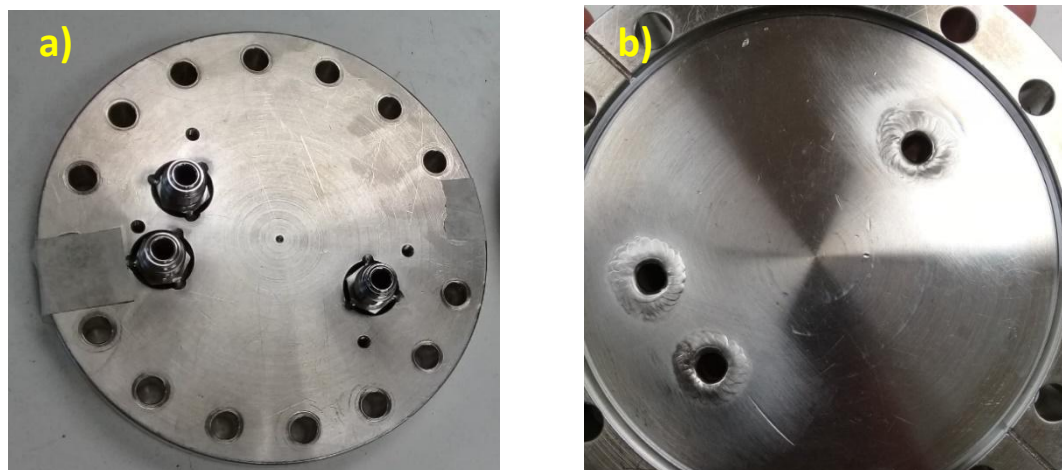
Piezas Bodies Bulkhead soldadas a la tapa brida. Vista superior a), e inferior b).
